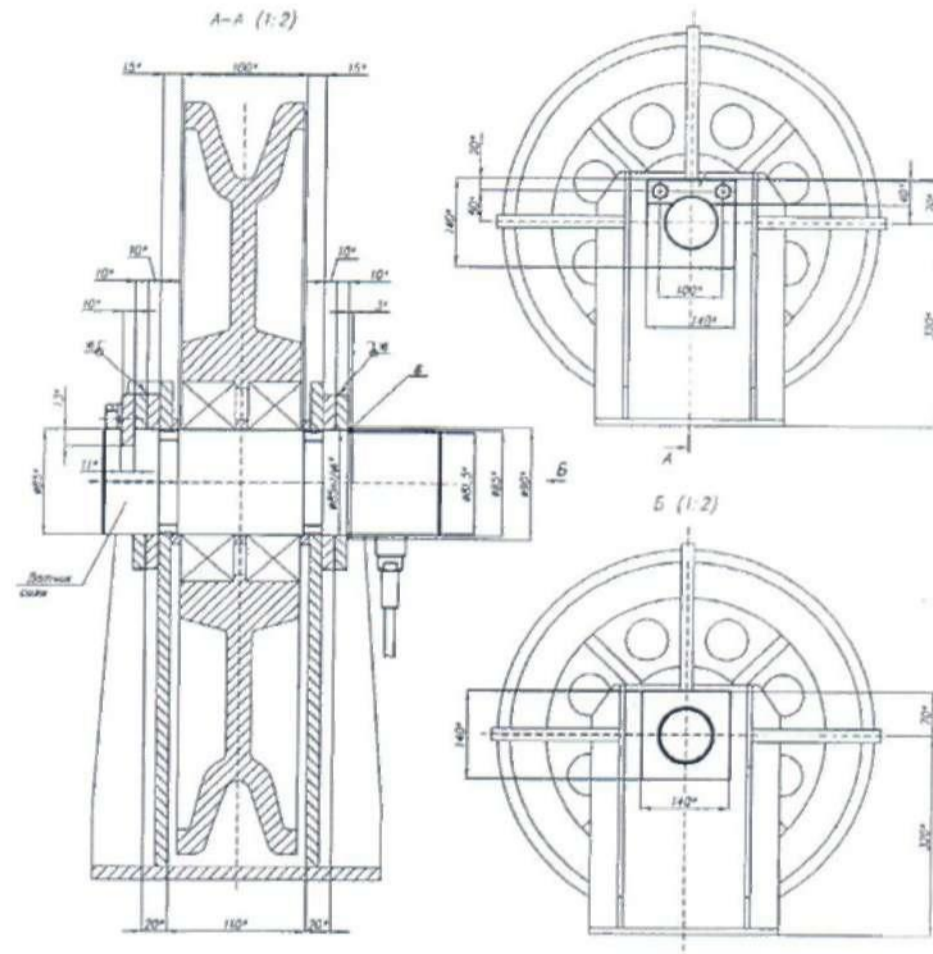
Габаритные и присоединительные размеры датчика усилия
